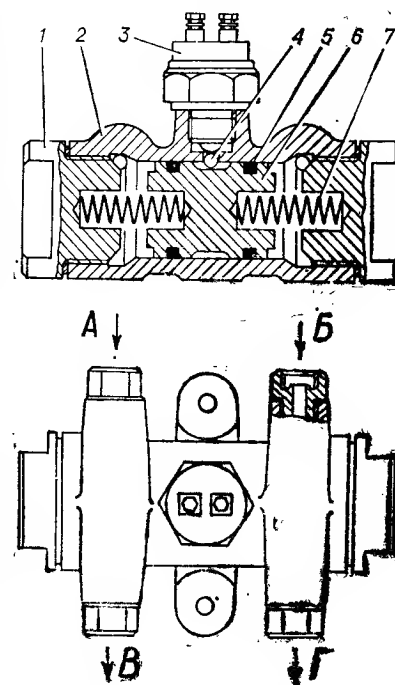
Уравнитель гидравлического привода рабочей тормозной системы:
